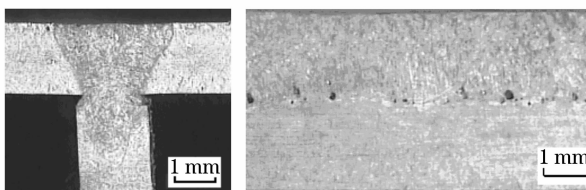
T 型接头激光焊接的焊缝横、纵截面
